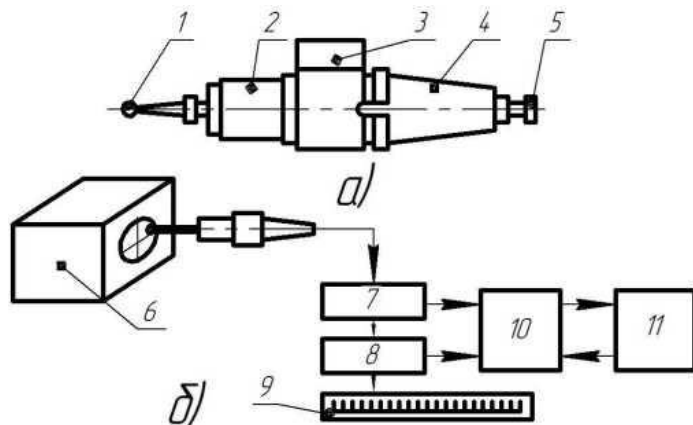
Пристрій автоматичного контролю на верстаті: а – датчик (1 – щуп; 2 – корпус; 3 – пристрій сигналізації; 4 – оправка; 5 – хвостовик); б – схема системи контролю (7 – пристрій пошуку сигналу; 8 – лічильник; 9 – пристрій зворотного зв'язку; 10 – пристрій контролю; 11 – пристрій ЧПК)
